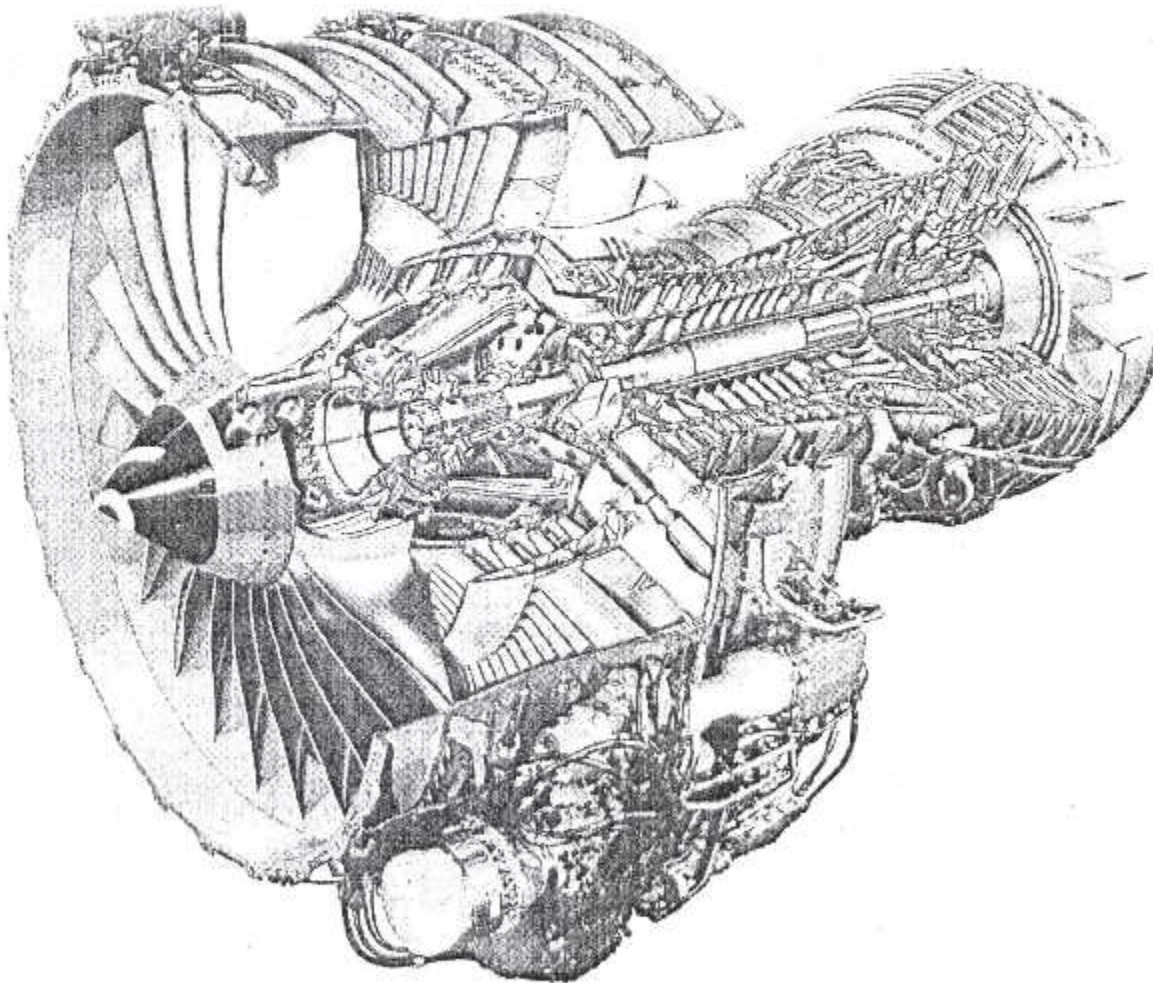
VUE GÉNÉRALE DU MOTEUR CFM56-7B
